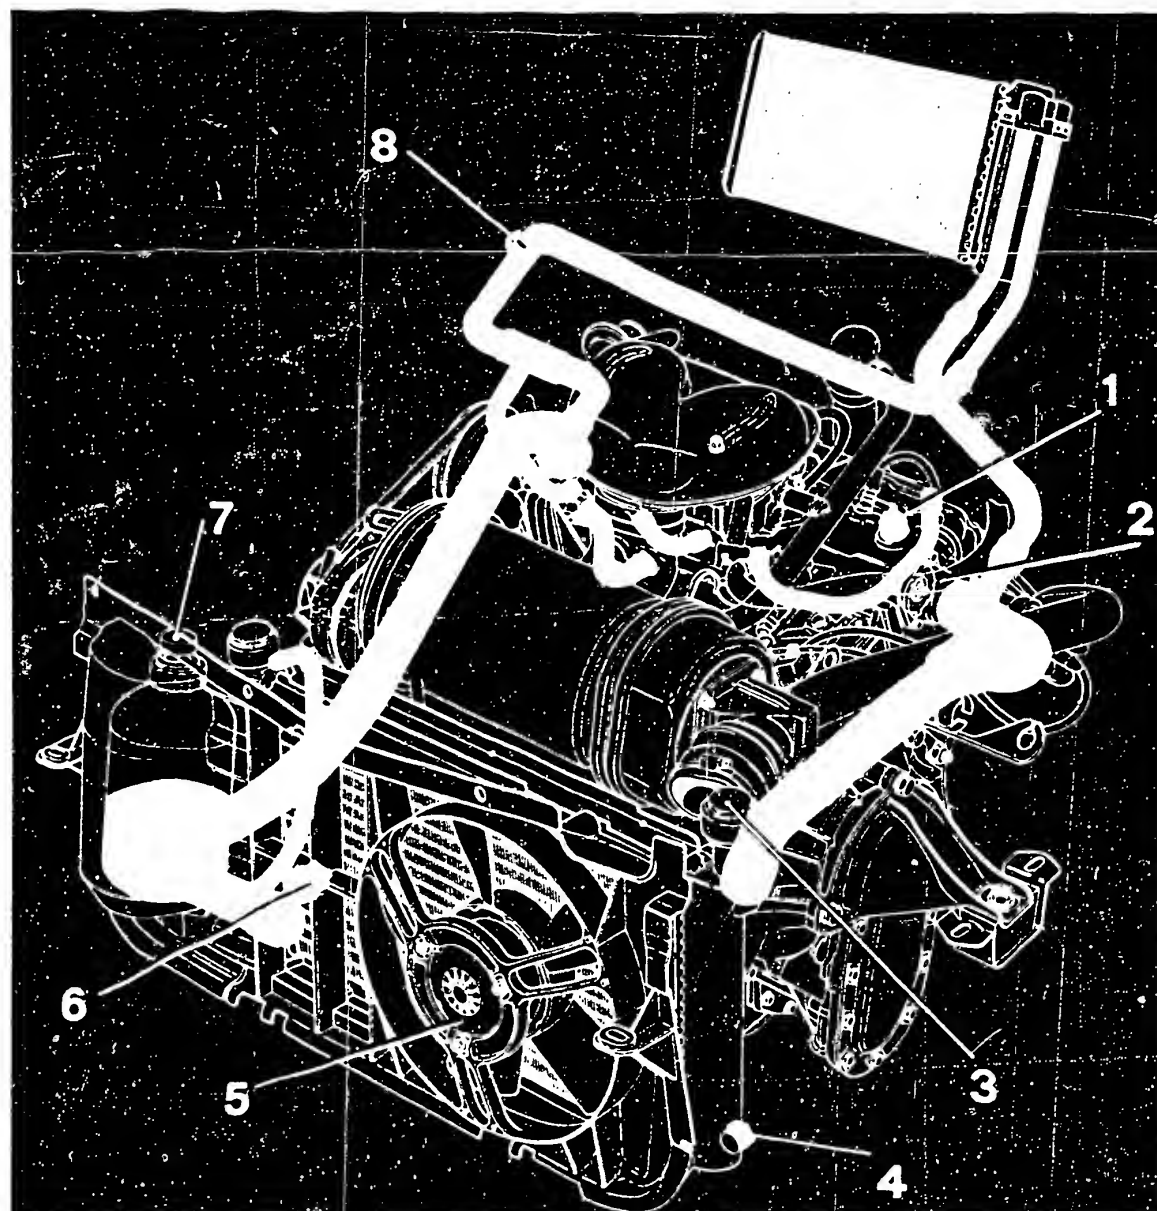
Das Kühlsystem mit den wichtigsten Komponenten: 1 Kühlwasser-Thermofühler – 2 Thermostat – 3 Einfüllstutzen – 4 Ablaszapfen – 5 elektrischer Lüfter – 6 Thermoschalter – 7 Expansionsgefäß mit Überdruckventil – 8 Entlüfterschraube.
